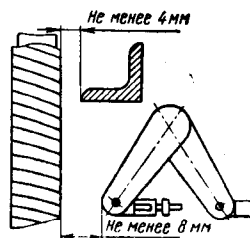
Зазор между трубопроводом, обшитым теплоизоляционным материалом, и неподвижными и подвижными элементами конструкции.
